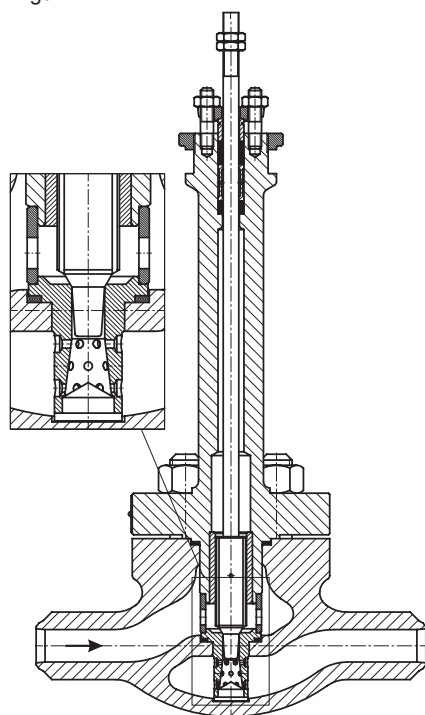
Zawór z grzybem obrotowym w zastosowaniu do pracy w warunkach flashingu
